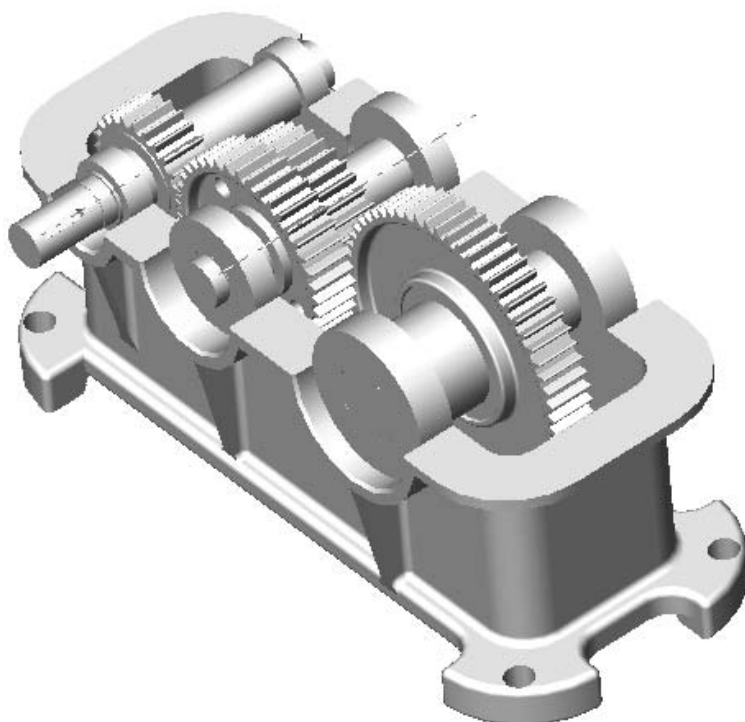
Трехмерная модель сборочной единицы корпуса редуктора с валами и подшипниками
